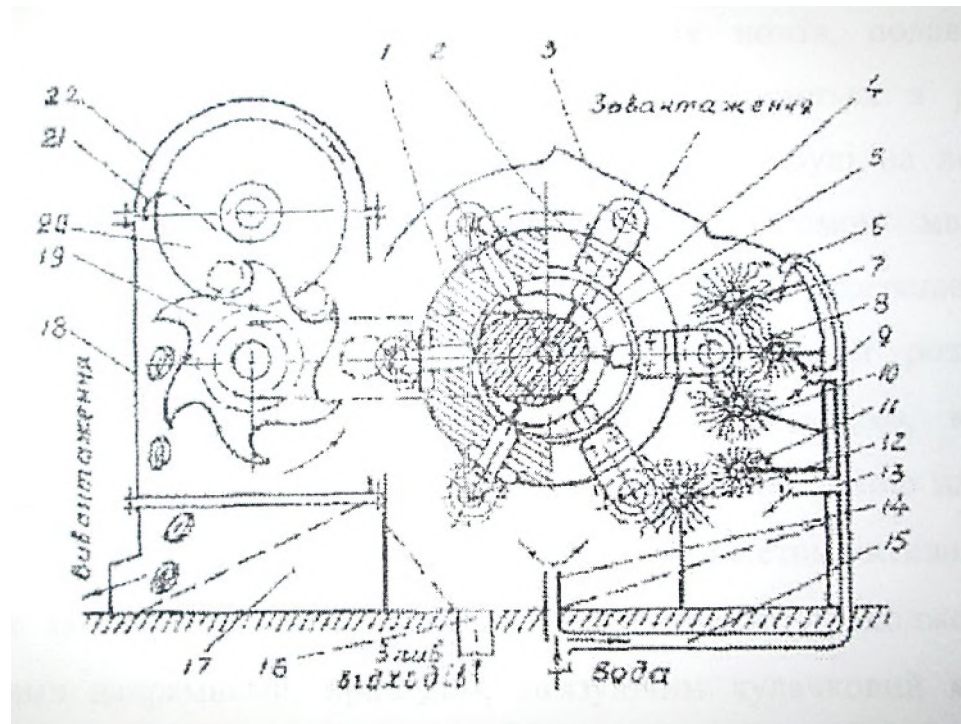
Загальний вигляд машини для обробки цибулі ББ-2-600
